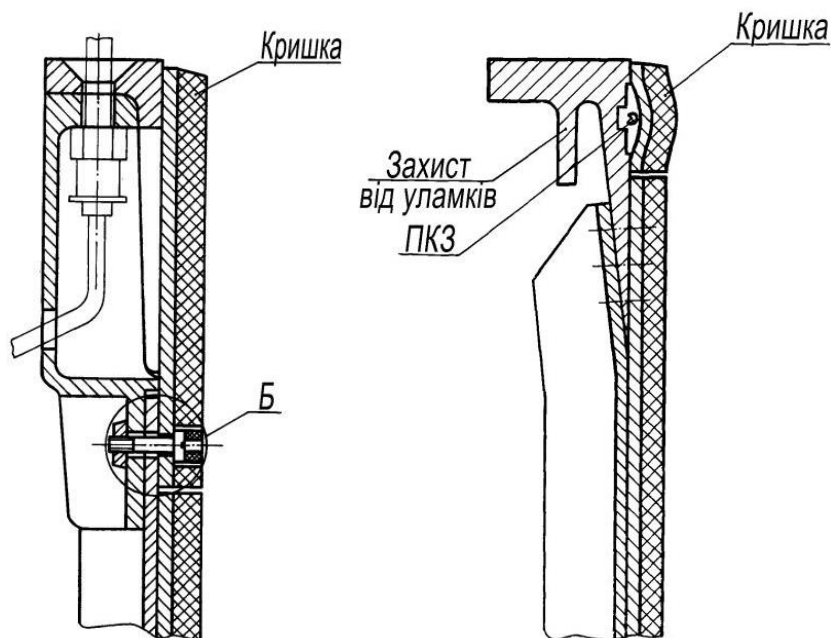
а) – установка піроболта; б) – установка ДПЗ
